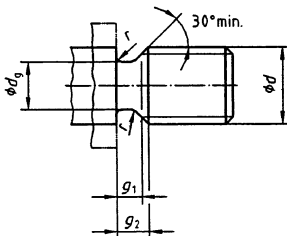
Gewindeauslauf (Maße s. Tab. 407.1)
